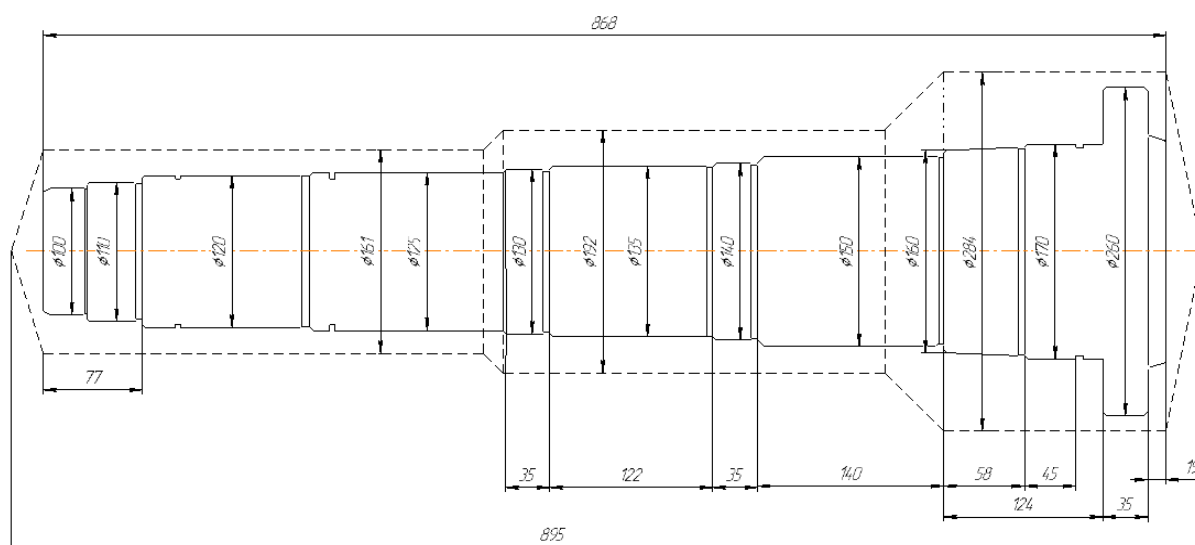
Метод получения заготовки штамповкой²
